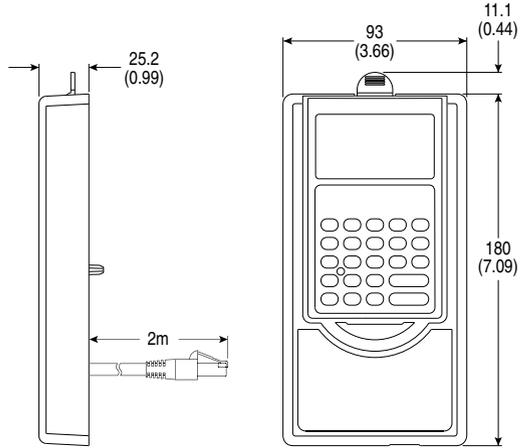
Módulo pequeño de interface de operador (montaje en panel) remoto –
